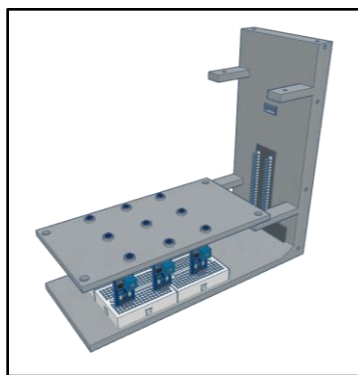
Ход сборки с P1 и P2, фотодиодами и платой интерфейса GPIO.
